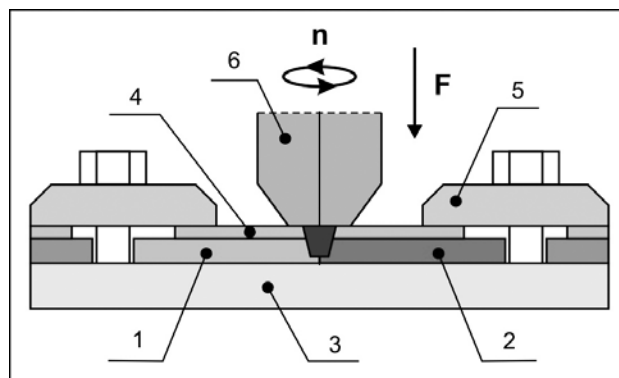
Условная схема процесса сварки трением с перемешиванием биметаллического соединения: 1 – алюминиевая пластина, 2 – медная пластина, 3 – металлическая подложка, 4 – накладная технологическая пластина, 5 – прижимы, 6 – инструмент
